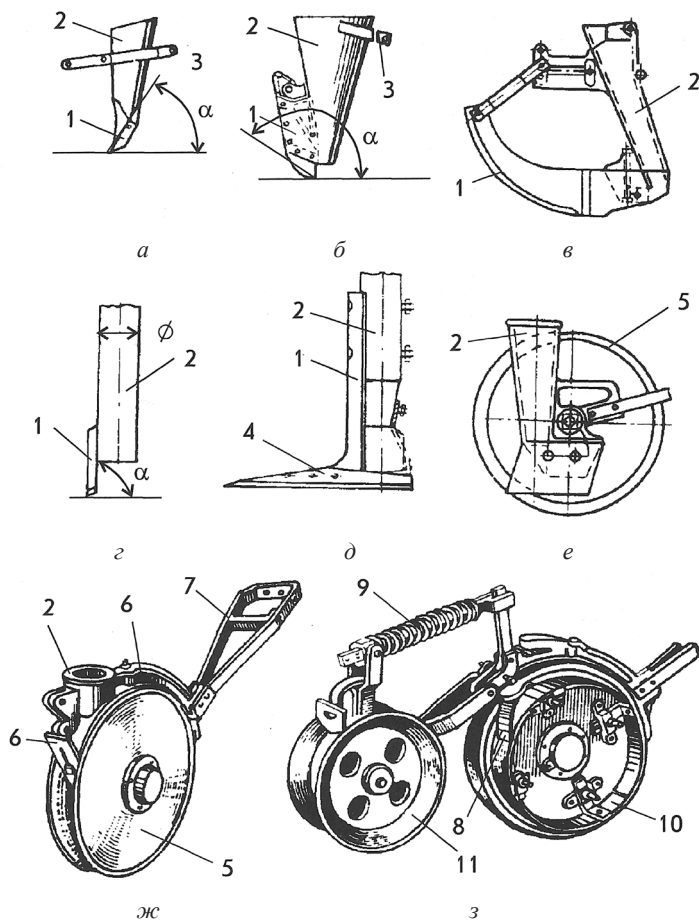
Сошники: а – анкерный; б – килевидный; в – полозовидный; г – трубчатый; д – лаповый; е – однодисковый; ж – двухдисковый; з – двухдисковый с ребрами; 1 – наральныйник; 2 – воронка; 3 – хомут; 4 – лапа; 5 – диск; 6 – корпус; 7 – поводок; 8 – чистик; 9 – пружина; 10 – ребра; 11 – каток
